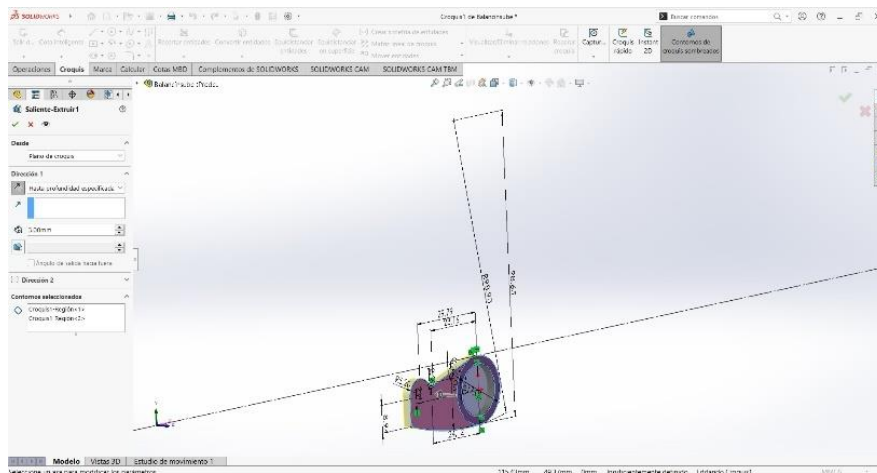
Balancín 1 (Extrusionado de Croquis 1). Fuente: SolidWorks
